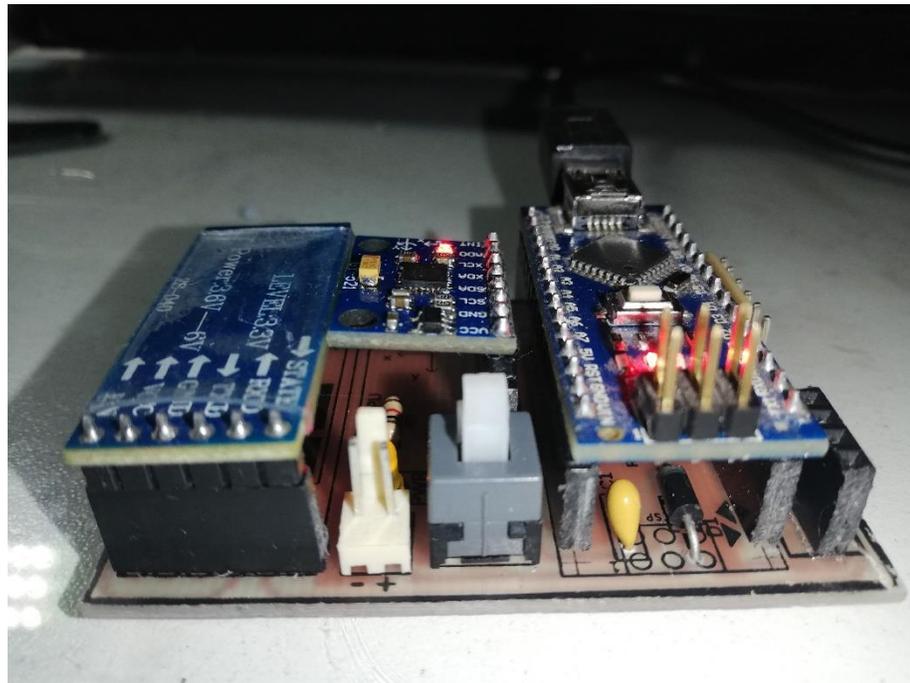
Placa PCB esclavo (Elaboración propia)
